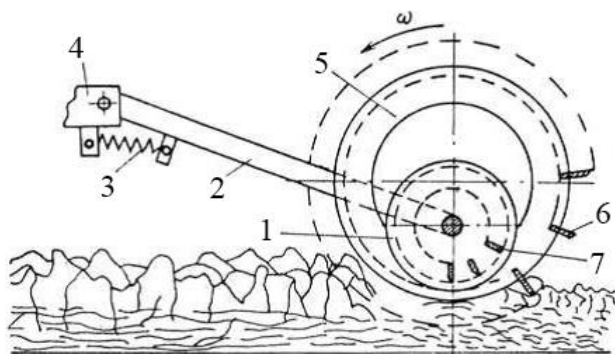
Конструктивна схема ґрунтообробного знаряддя: 1, 5 – внутрішній і зовнішній барабани; 2 – шарнірний поводок; 3 – пружинний довантажувач; 4 – рама культиватора; 6, 7 – радіальні планки барабанів.
